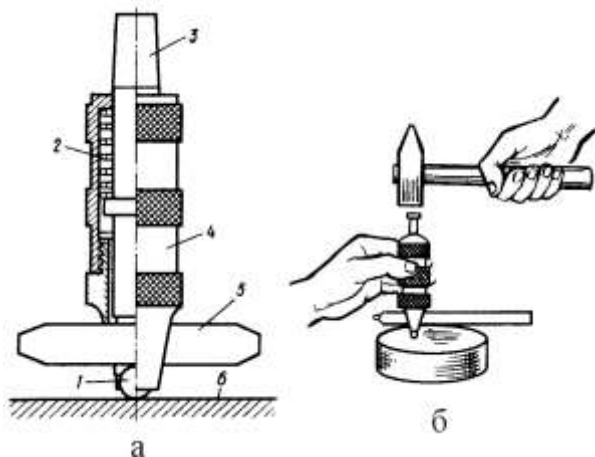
Прилад для вимірювання твердості металів методом ударного відбитка: а – конструкція приладу; б – схема визначення твердості; 1 – куля; 2 – пружина; 3 – бойок; 4 – корпус; 5 – еталон; 6 – контрольований виріб
